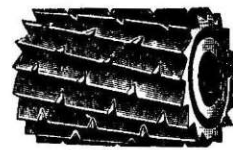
Цилиндрический осевой фрезер со спиральным зубом и стружколомателем.
